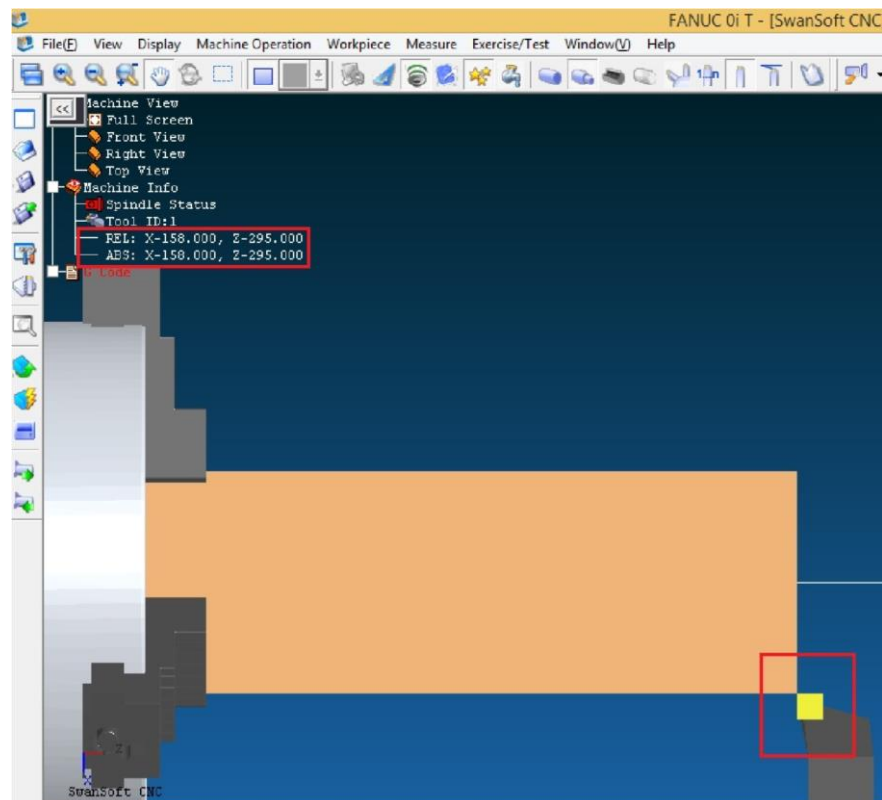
Переміщення різця впритул до торця заготовки
